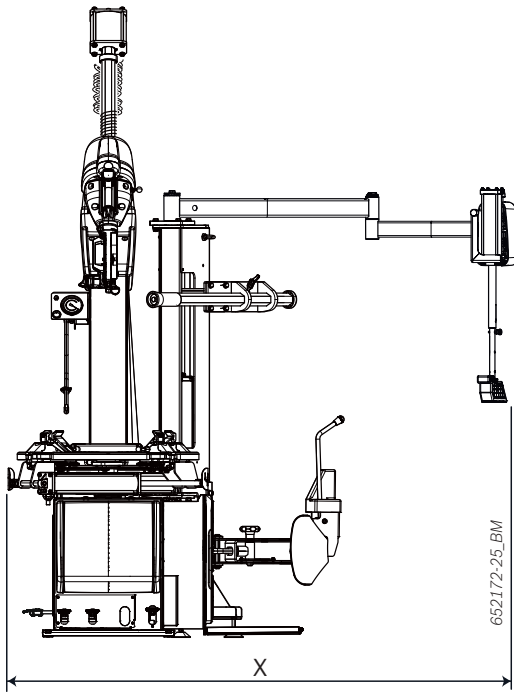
Dimensions de FALCO EVO 628 S (IT) V8 (vue de face)
